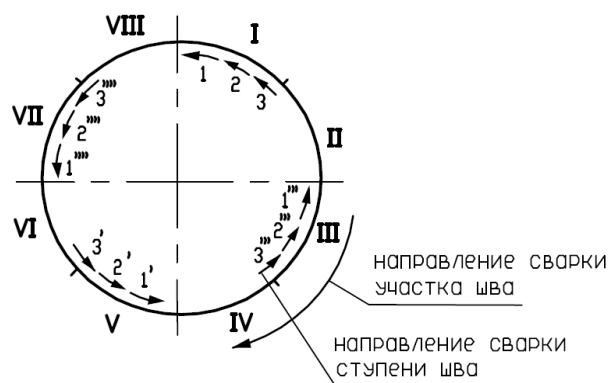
Последовательность сварки параллельных швов
